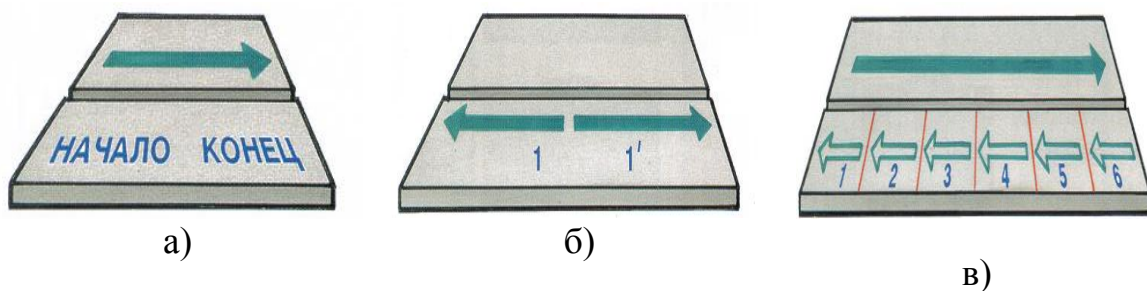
Способы выполнения сварных швов по длине
